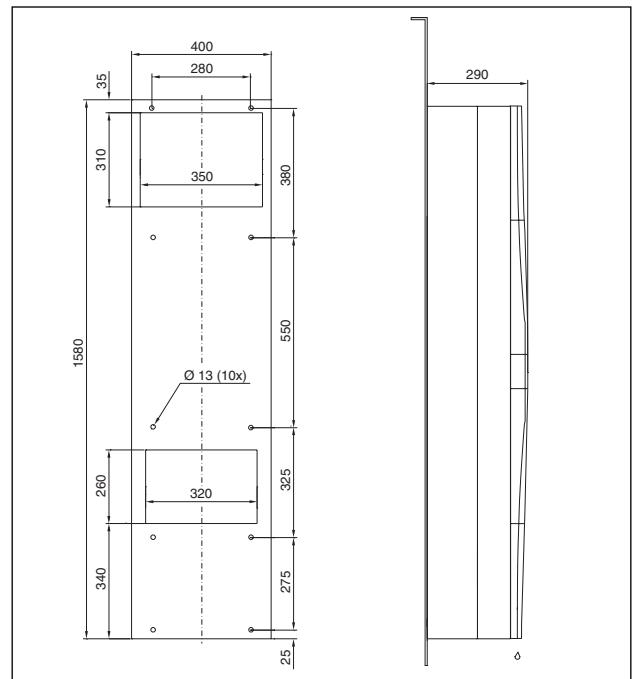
SK 3328.xxx, SK 3329.xxx Påbyggnad
